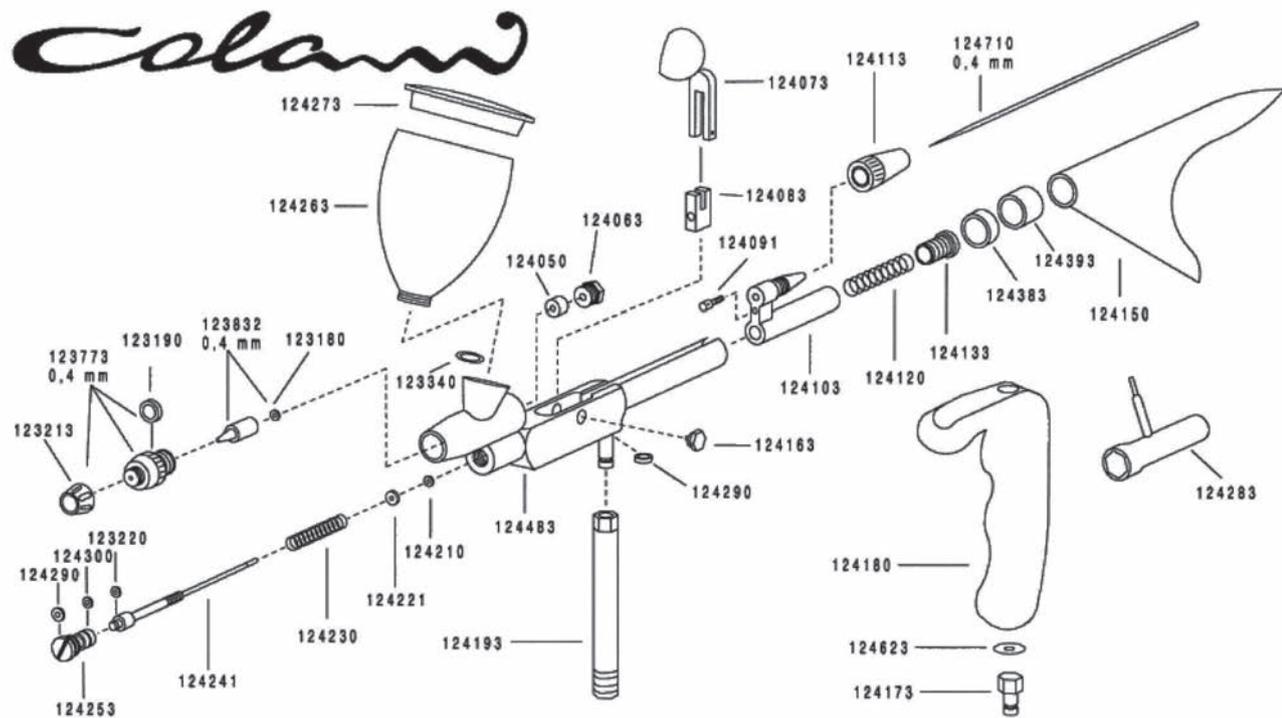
Desenho técnico (Vista Explodida) projeto Colani.
